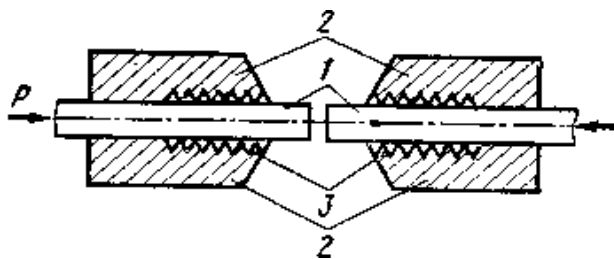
Схема стикового холодного зварювання: 1 – деталі, що з'єднуються; 2 – затискачі (губки машини); 3 – насічки на губках
